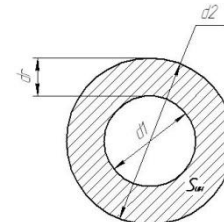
Изображение торца кольцевого сварочного инструмента
